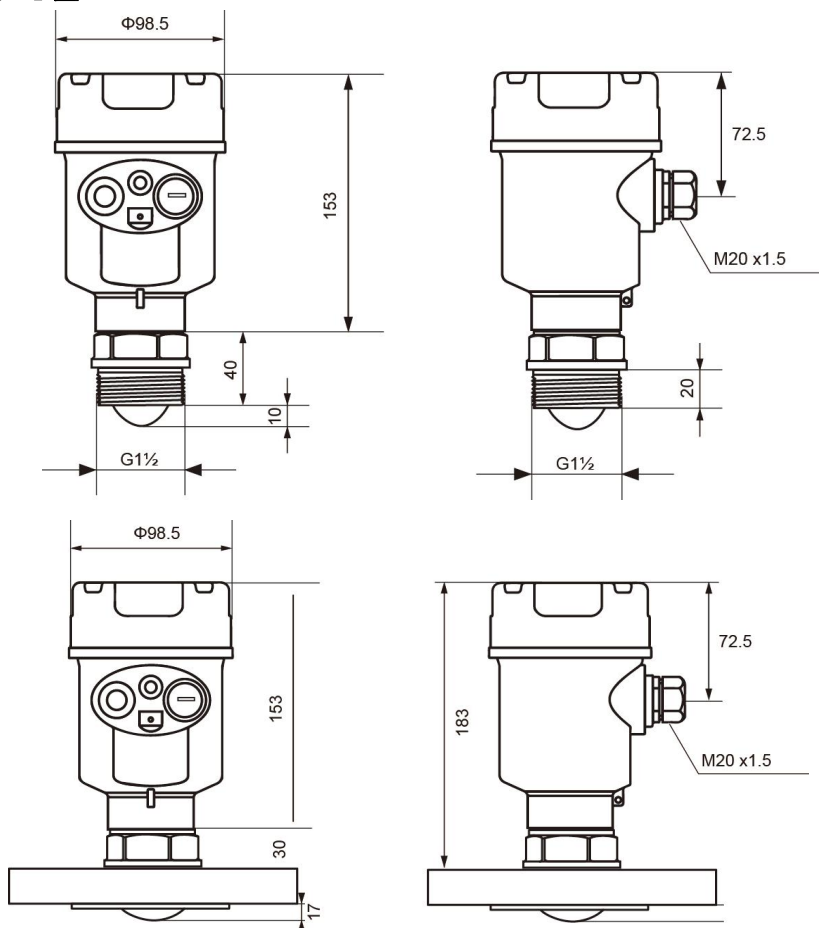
I 型雷达物位计外形尺寸图 (单位: mm)
